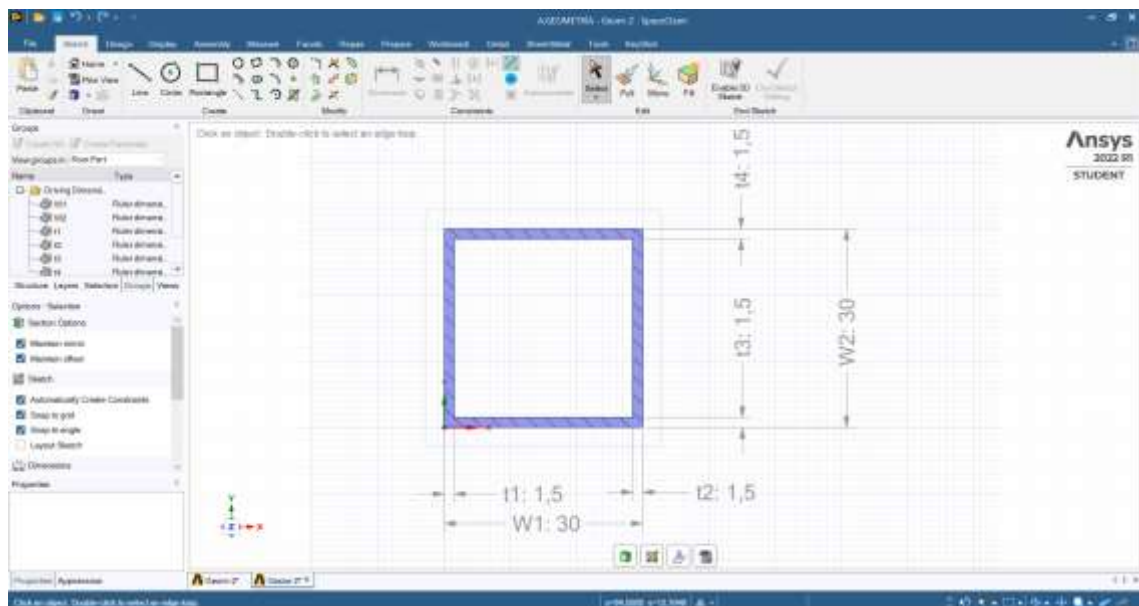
Dimensiones del perfil cuadrado 30 x 1,5 [mm]
